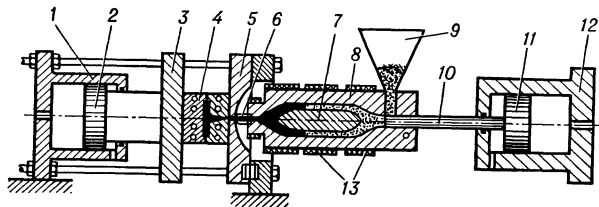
Литьевая машина поршневого типа: 1 — гидравлический цилиндр; 2 — плунжер; 3 — подвижная плита; 4 — литьевая форма; 5 — неподвижная плита; 6 — сопло; 7 — торпеда; 8 — инжекционный цилиндр; 9 — бункер; 10 — поршень; 11 — плунжер; 12 — гидравлический цилиндр; 13 — электрообогрев.
